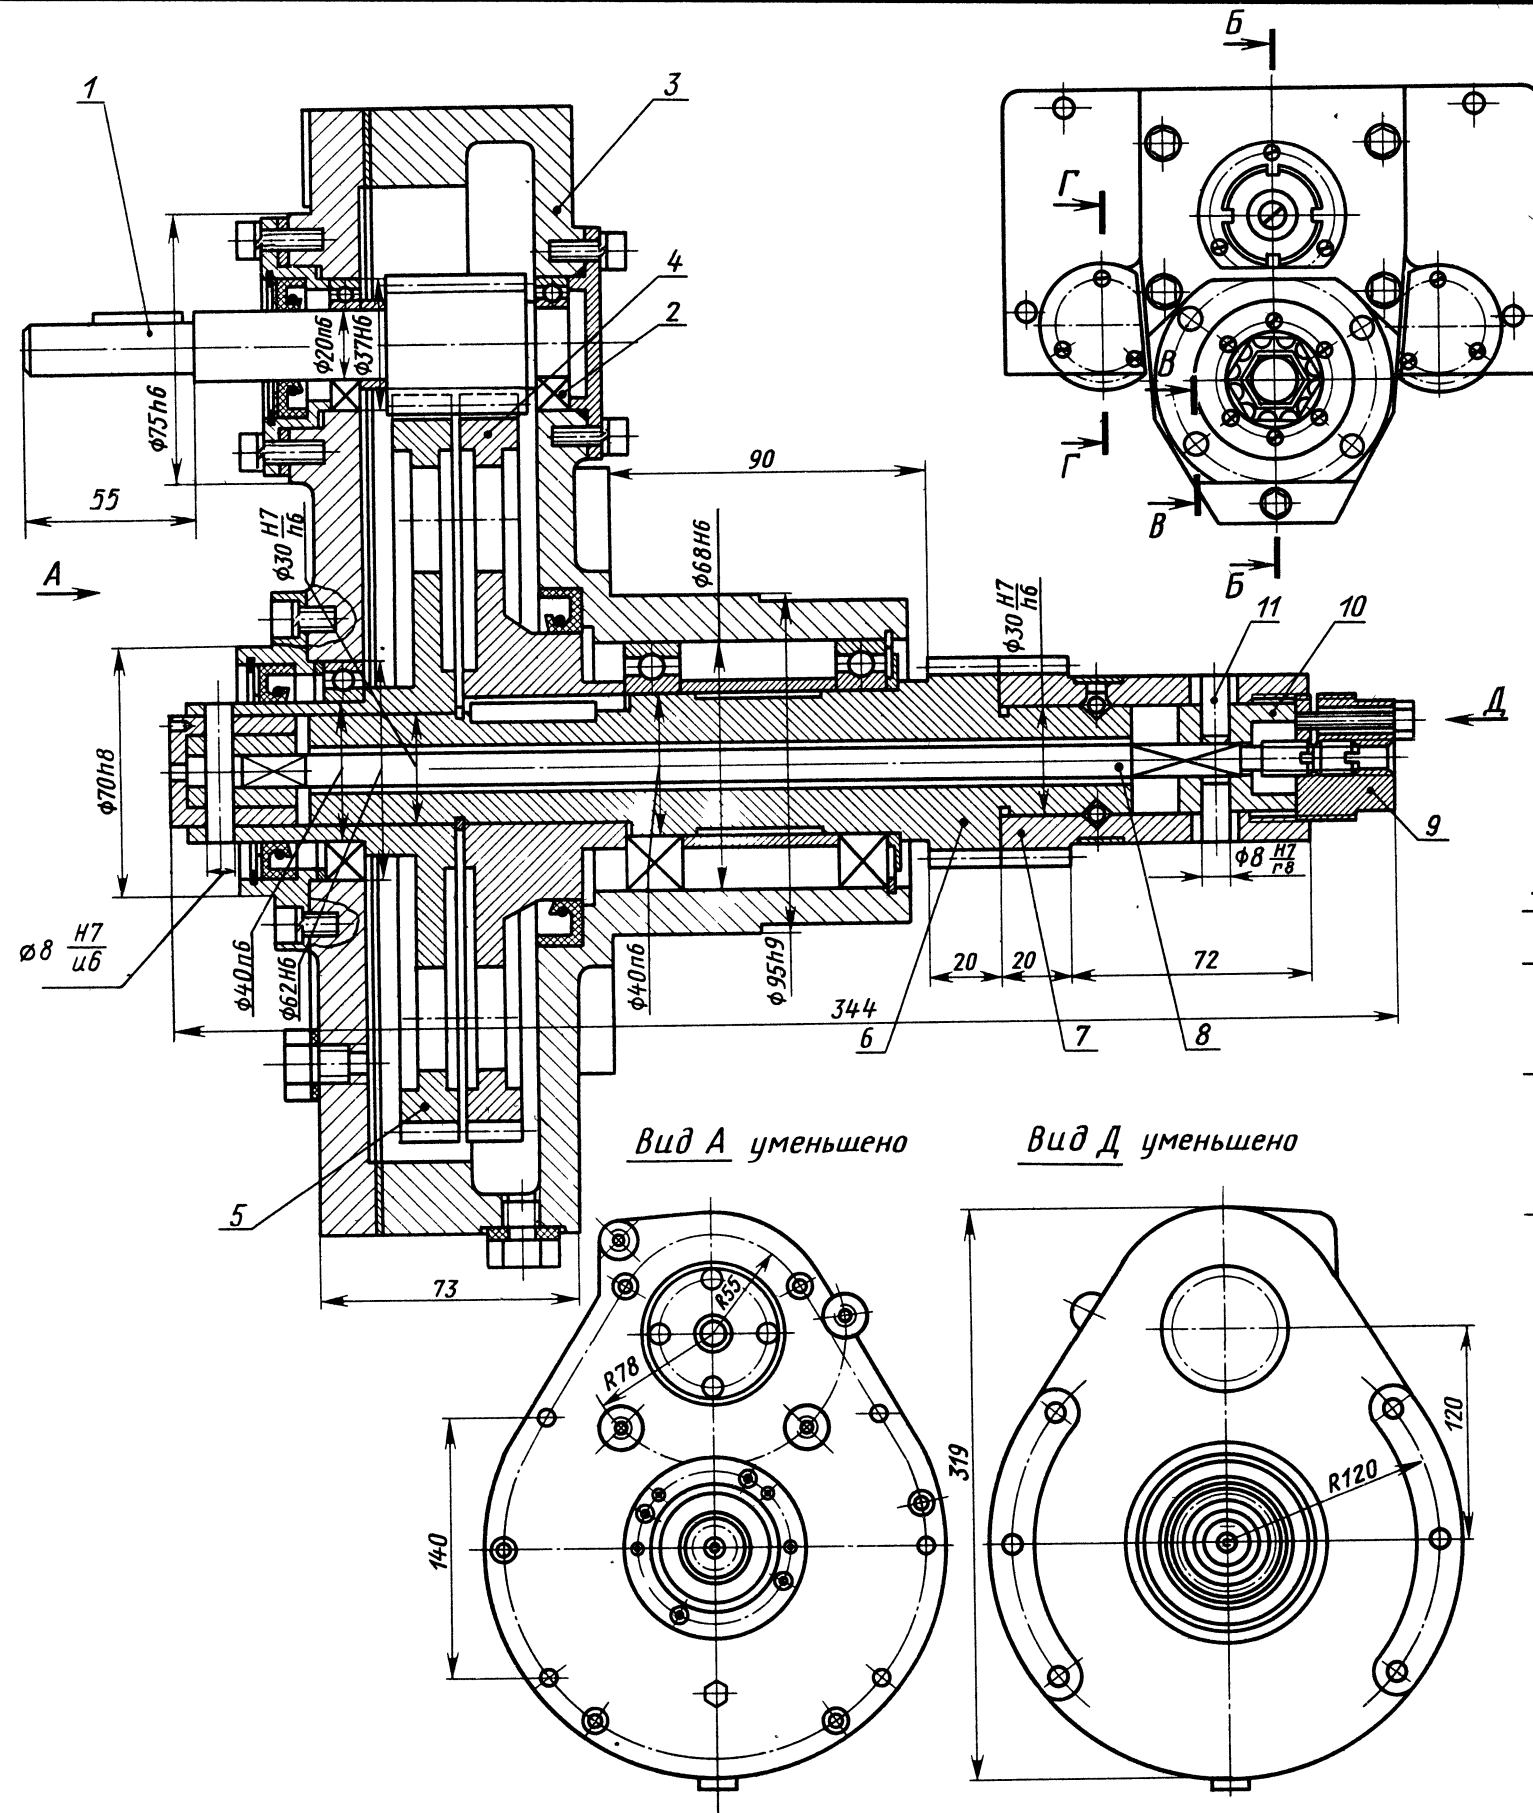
Механизм привода руки с зубчатым редуктором для ПР РГШ-40
